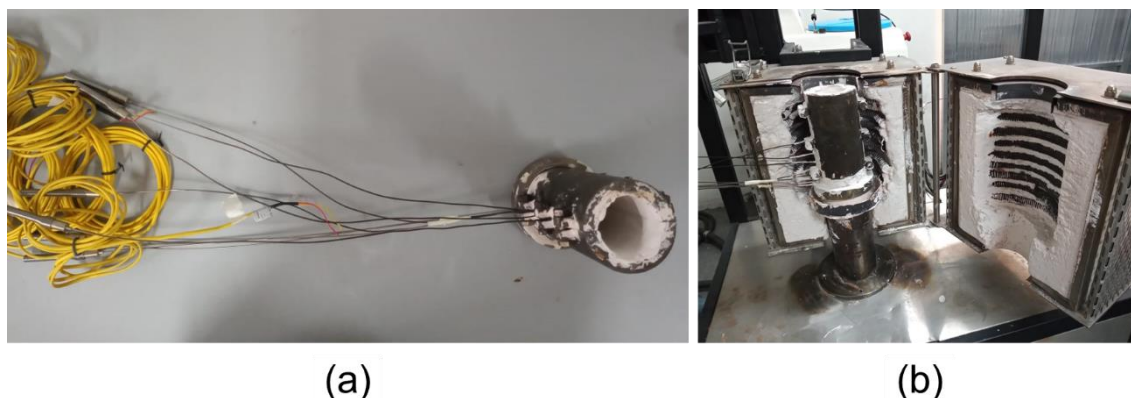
Preparo do molde bipartido. a) Com os termopares posicionados; b) Posicionado no forno de solidificação direcional.
